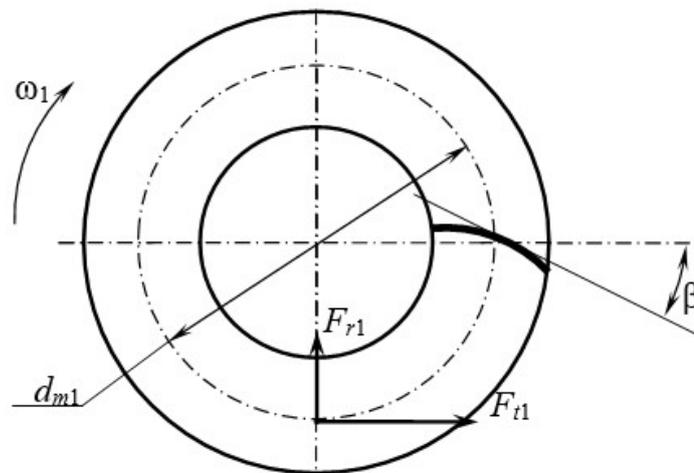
Коническая шестерня с круговым зубом (вид со стороны вершины конуса)
